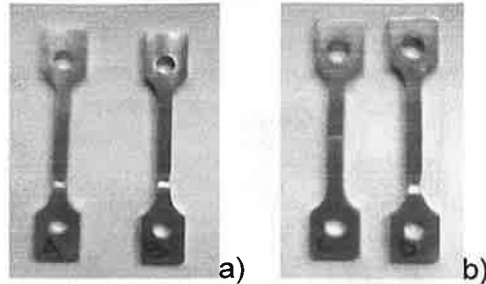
Probetas ensayadas a tensión en la MTS, (a) material base,(b) unión soldada.
